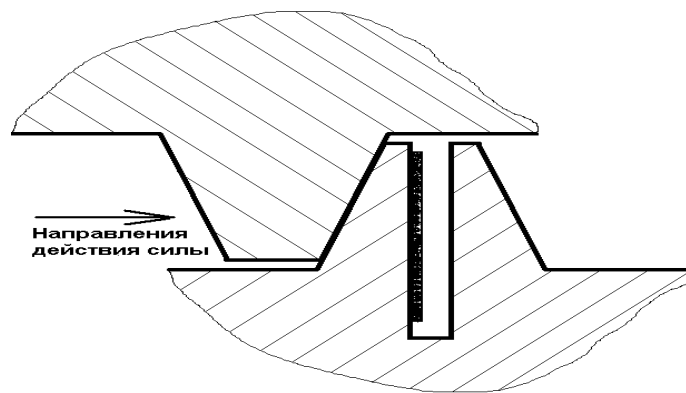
Схема установки тензорезистора на щеку прорези зуба
